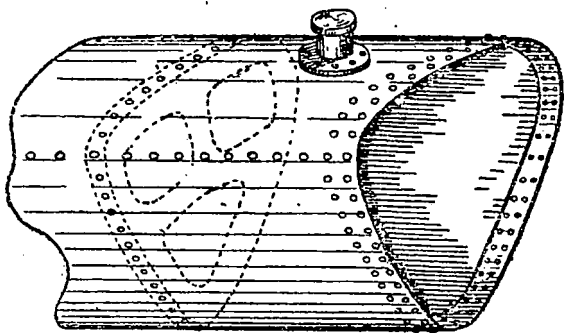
Заклепочный шов дуралюминового бака; *a*—заклепки с прокладками, *b*—пен ковая прокладка, пропитанная шеллаком.
